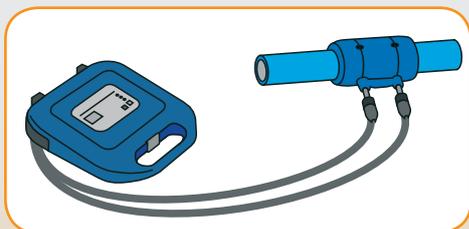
Схема сварки с помощью электромуфты (в соответствии с инструкцией изготовителя электрического сварочного аппарата).
